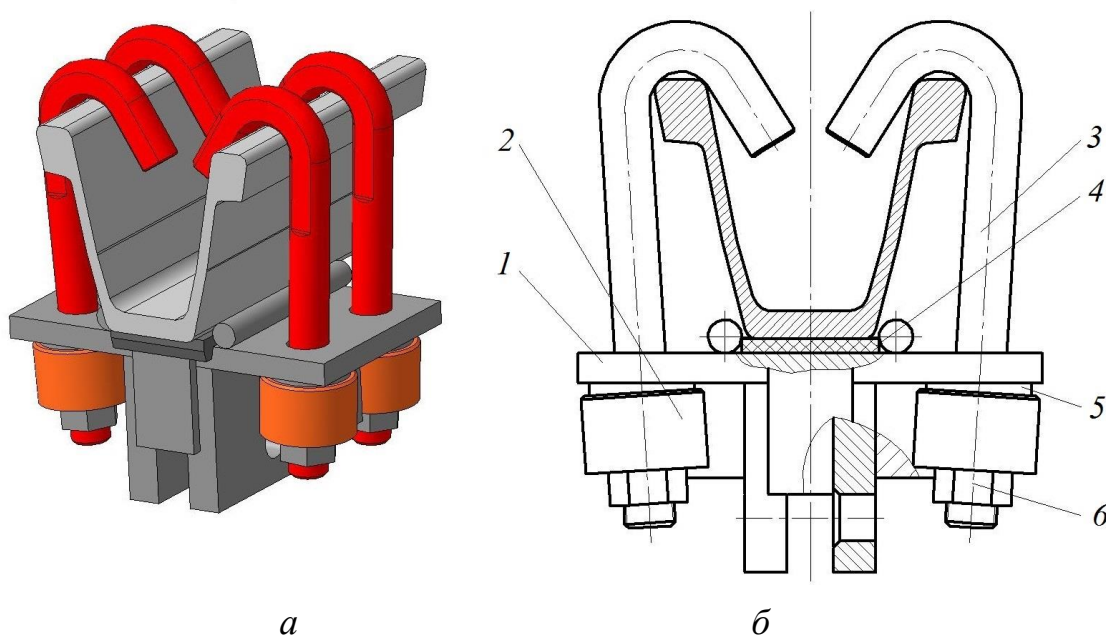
Подвес монорельсового пути для крепления к арочной крепи: *а* – общий вид; *б* – принципиальная схема, где 1 – корпус; 2 – вязко-упругое устройство; 3 – арочный болт; 4 – эластичная прокладка; 5 – косая шайба; 6 – гайка
